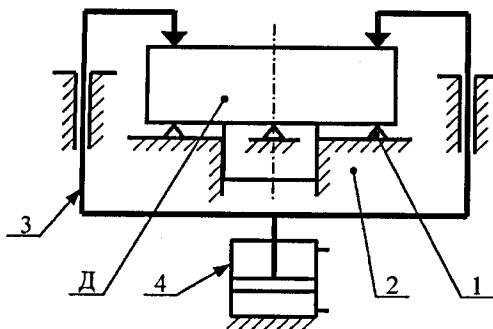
верстатне пристосування з прихватами і пневмоциліндром двосторонньої дії: 1 – установні опори, 2 – корпус, 3 – прихвати, 4 – пневмоциліндр
